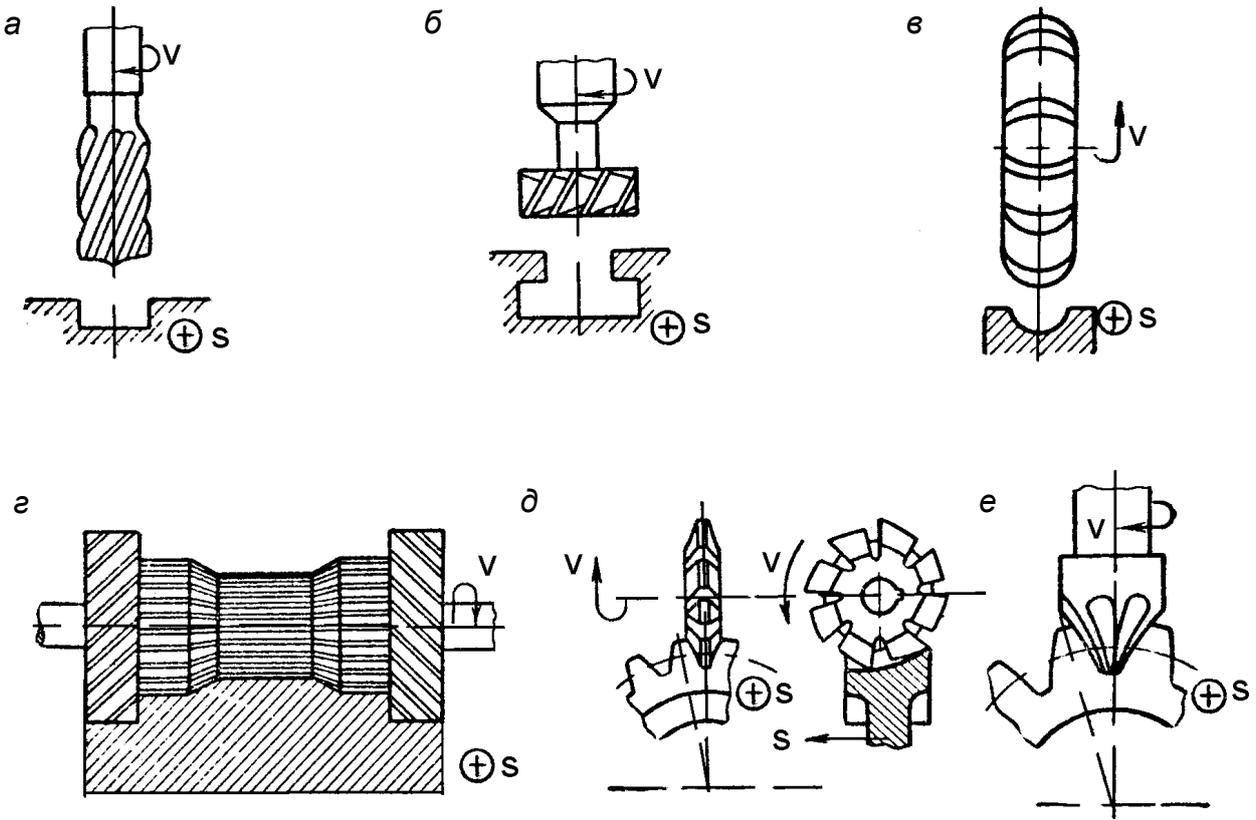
Основные виды фрезерования пазов, канавок, фасонных поверхностей и зубчатых колес: а – обработка прямоугольных пазов концевыми фрезами; б – обработка Т-образных пазов торцовыми фрезами; в – обработка фасонных поверхностей фасонной фрезой; г – обработка фасонных поверхностей набором простых фрез; д – обработка зубчатых колес дисковыми модульными фрезами; е – обработка зубчатых колес модульными пальцевыми фрезами
